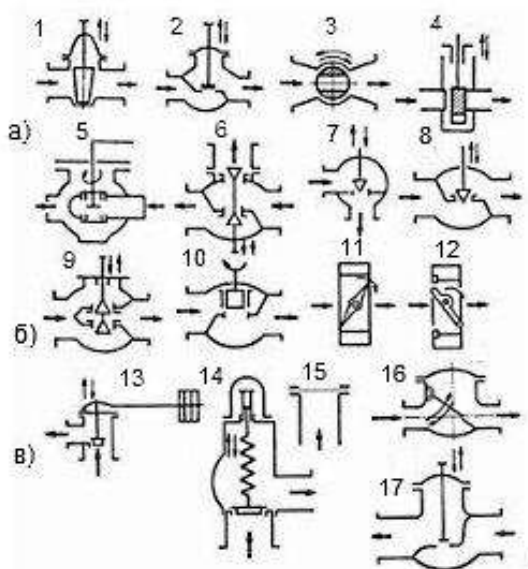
Основные типы трубопроводной арматуры АЭС:
